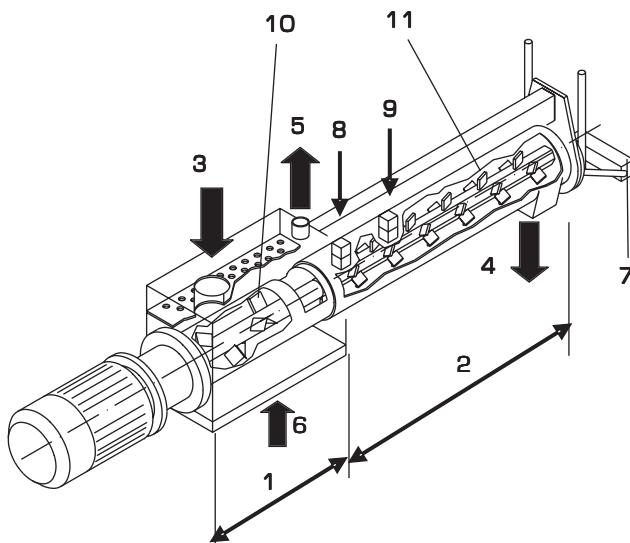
Устройство камеры очистки песка и зоны смешивания:
